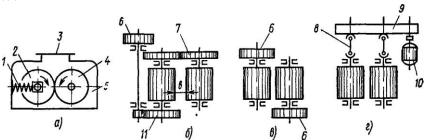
Схемы двухвалковой дробилки (а) и привода валков (б - г):
